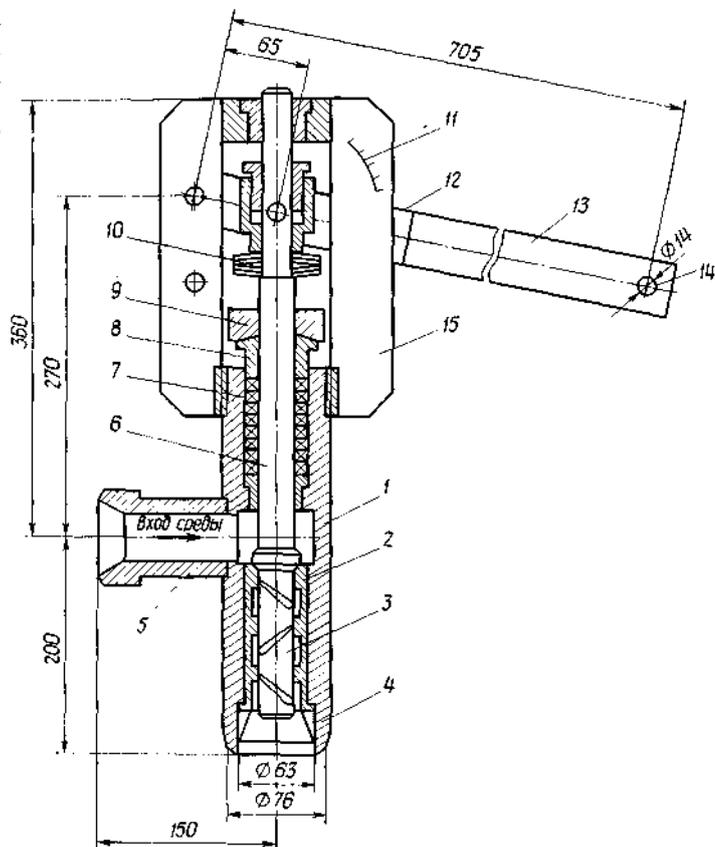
Клапан регулирующий многоступенчатый D_v 65 серии 879
